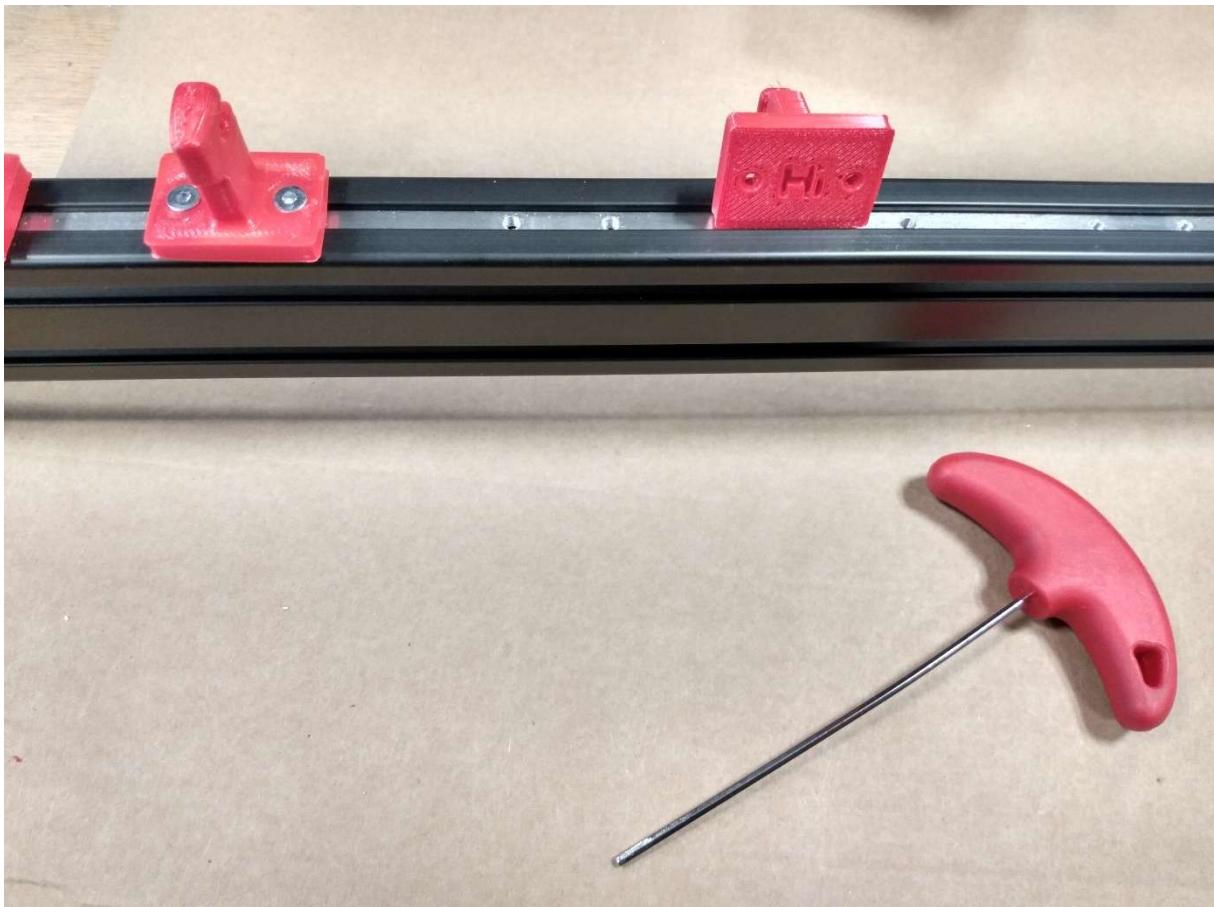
Plattenhalter-Einbau (Halter mit Kennzeichnung)
